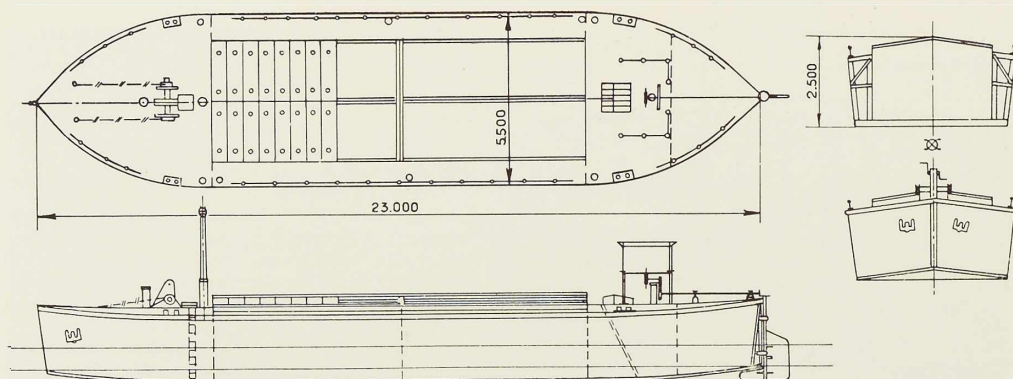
Plan, élévation et coupes d'un chaland soudé en service en Palestine.
